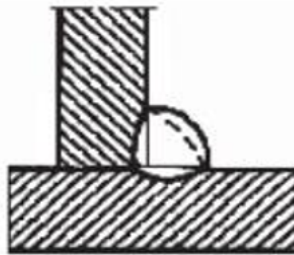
Эскиз дефекта сварного шва
